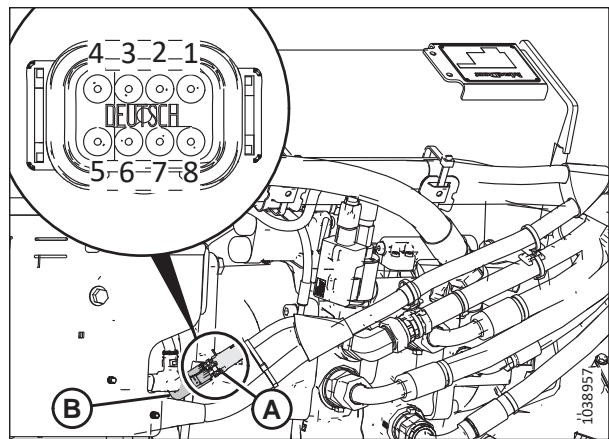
Connettore P600 – Vista dalla parte posteriore
